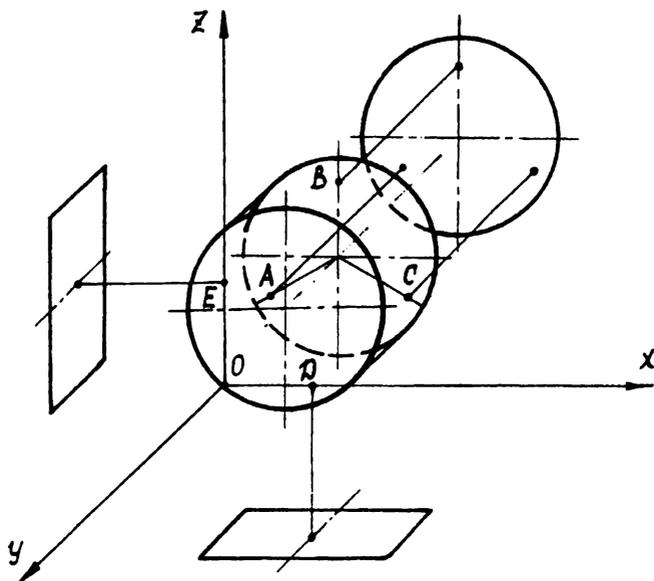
Схема базирования дисков: три опорные точки A , B , C на торце; две опорные точки D , E на цилиндре
